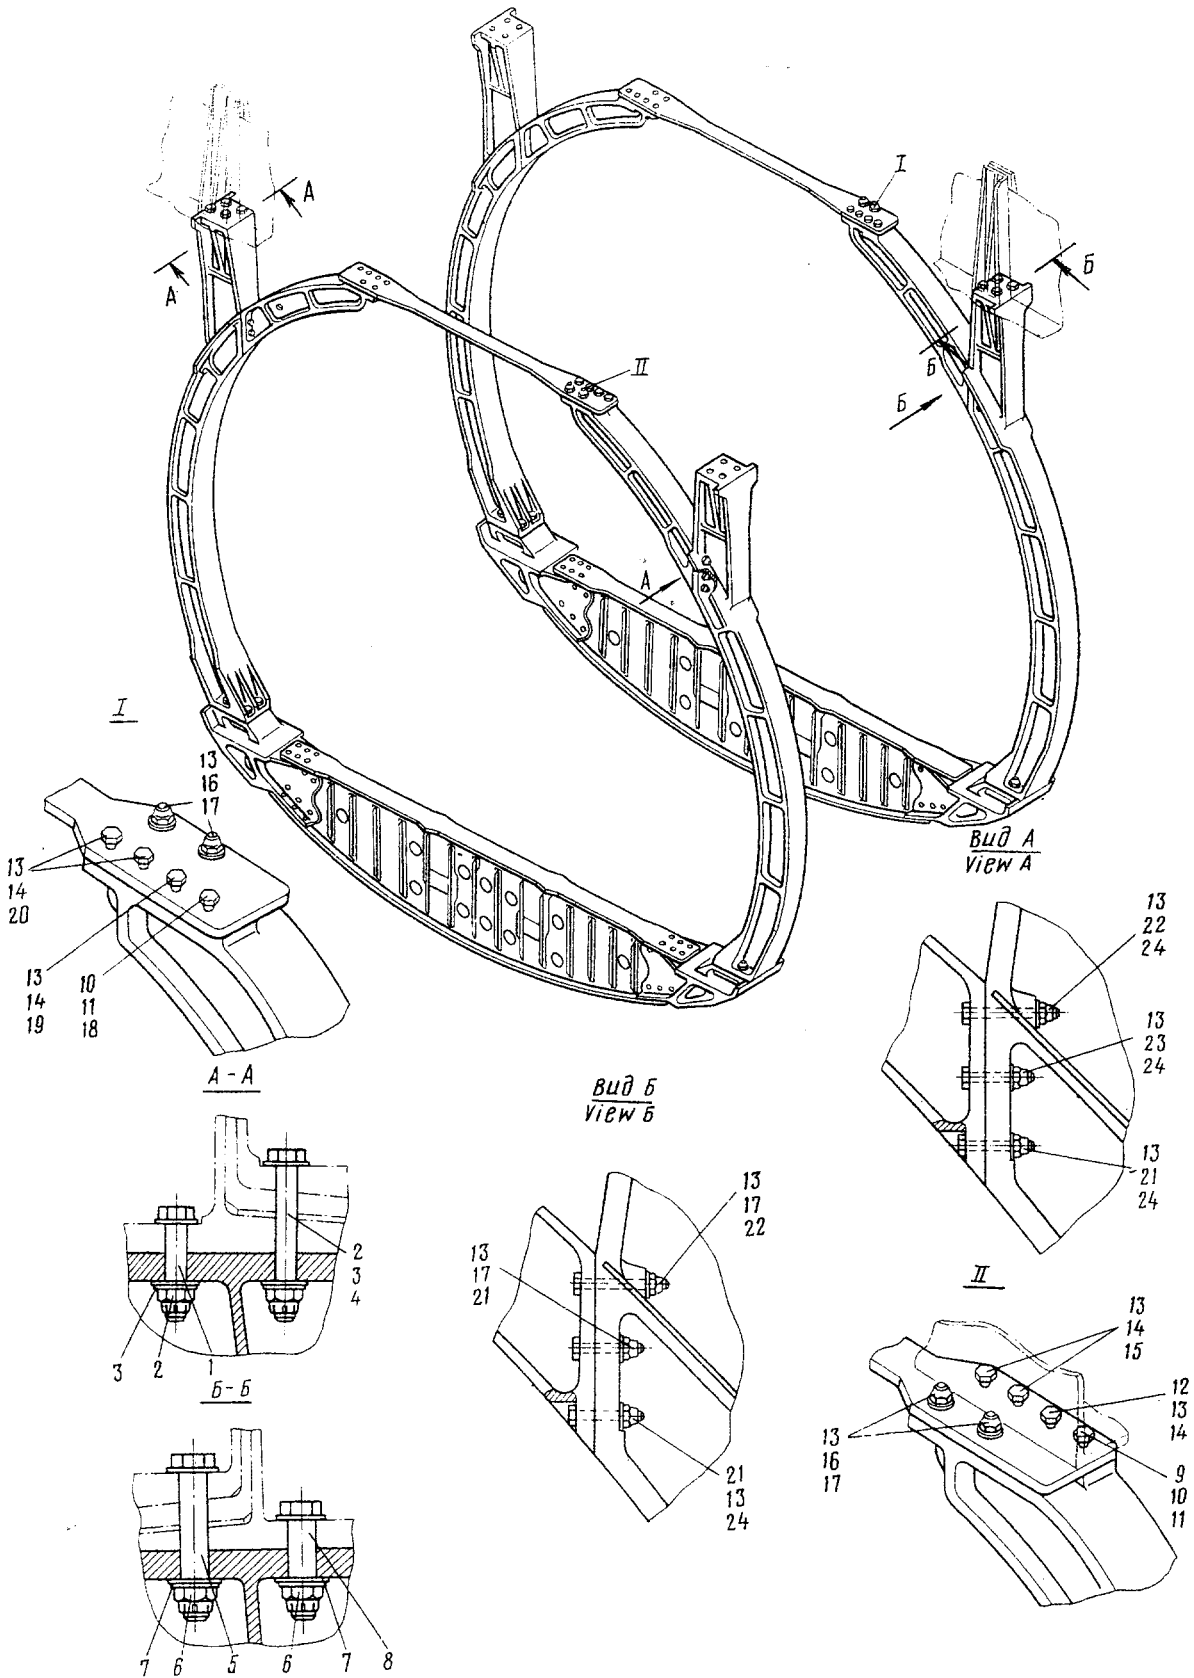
СТЫК ФЮЗЕЛЯЖА С ЦЕНТРОПЛАНОМ
